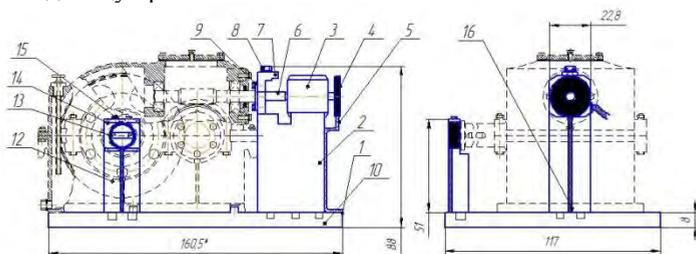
Схема редуктора и контрольно-регулирующего приспособления
